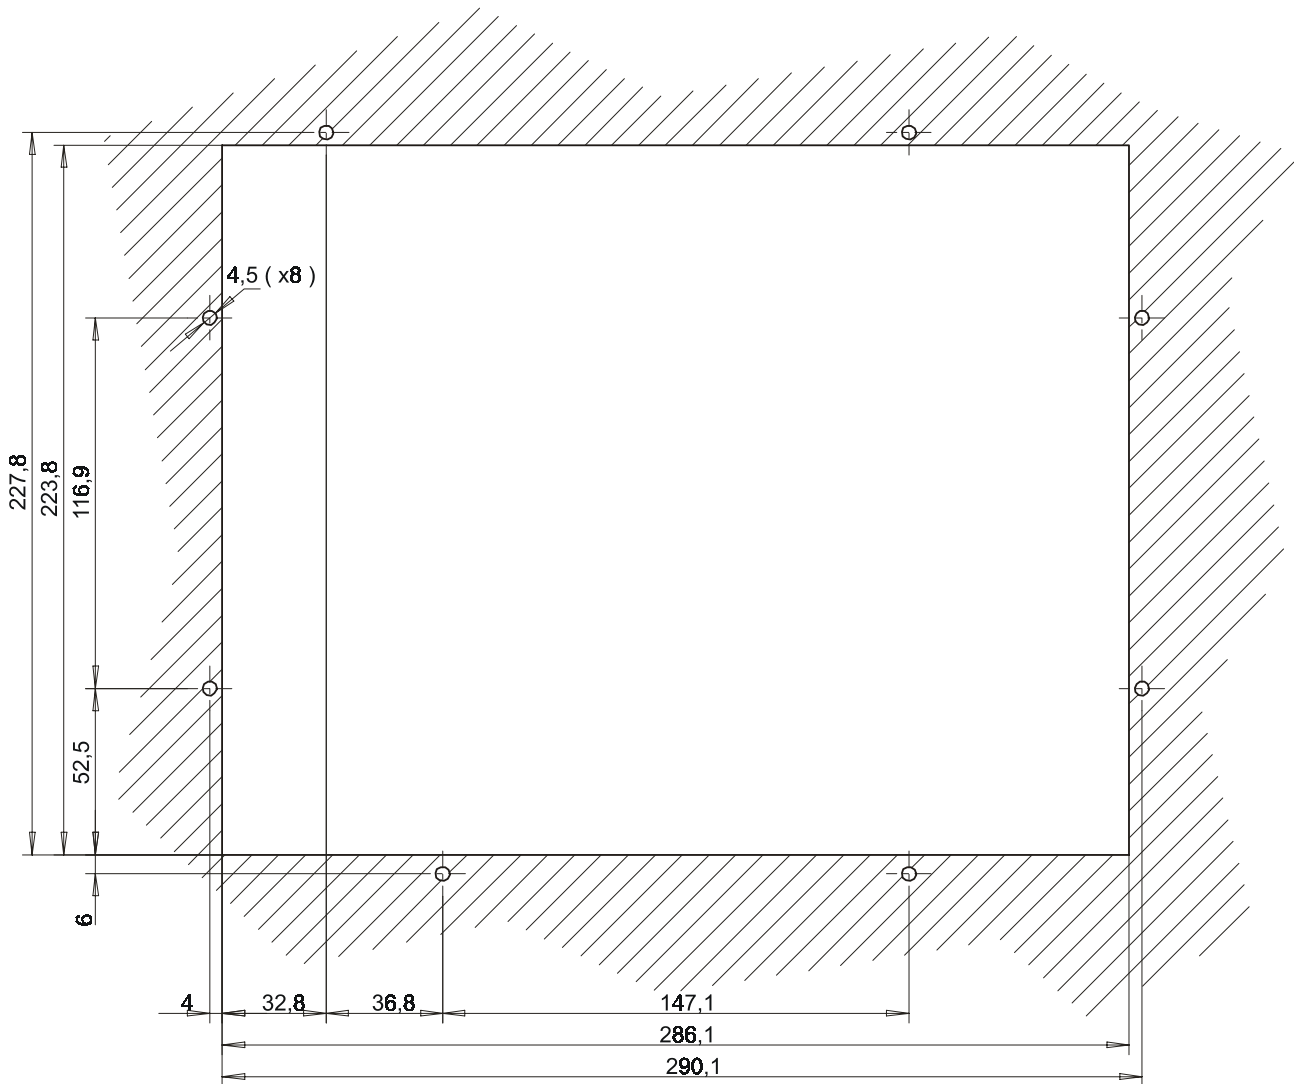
Maßzeichnung für Frontausschnitt CMP1 (alle Angaben in mm)
